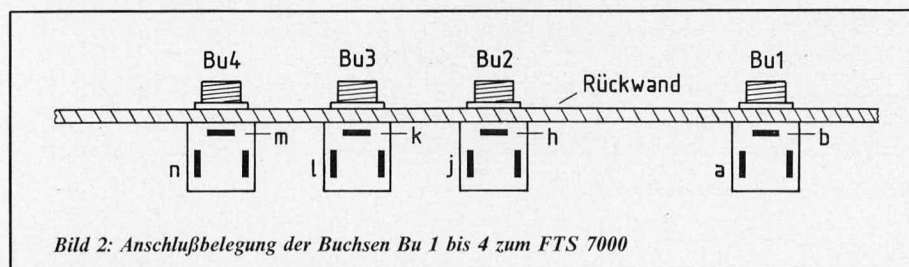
Anschlußbelegung der Buchsen Bu 1 bis 4 zum FTS 7000
